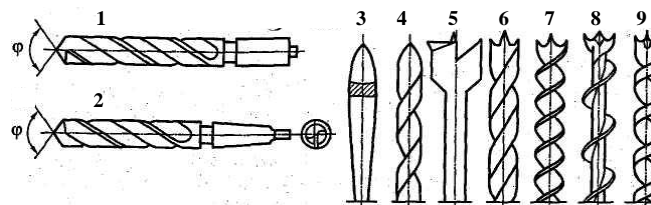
Сверла для работы по металлу (1, 2) и дереву (3-9)
